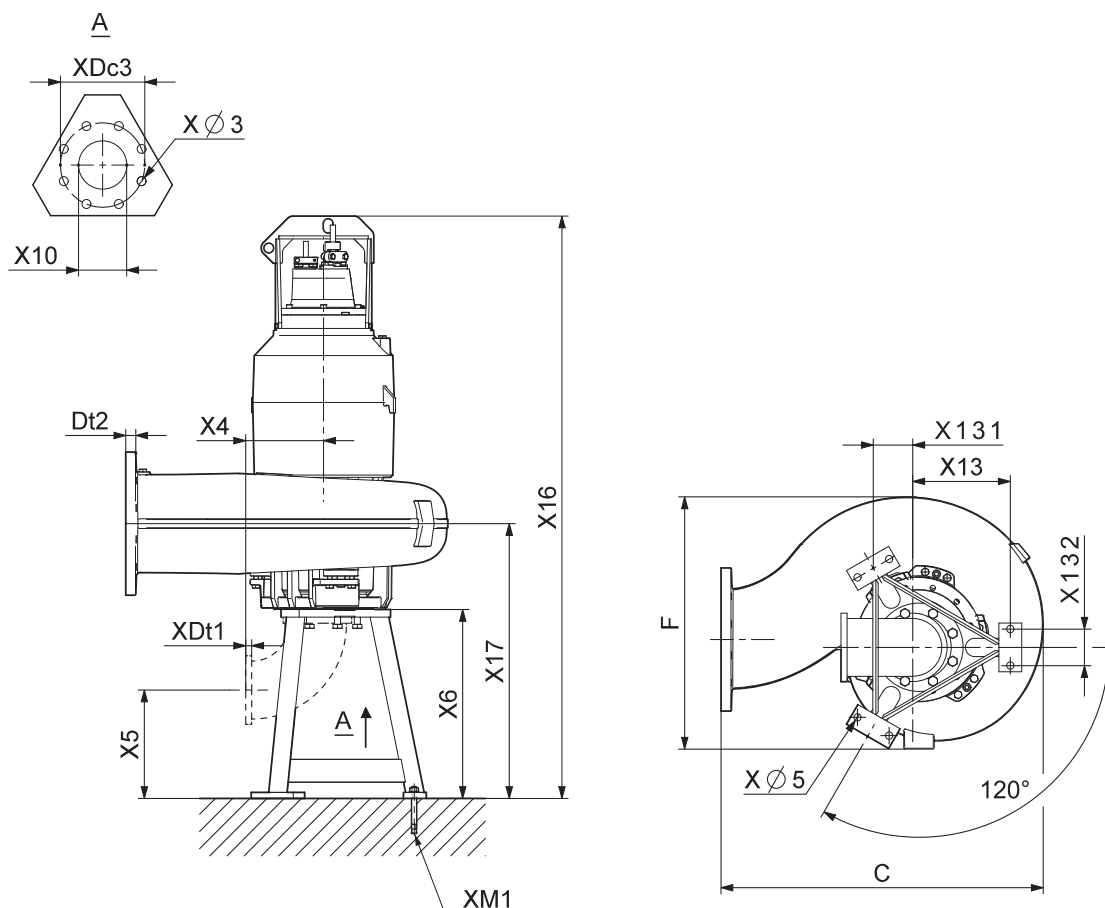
Габаритные размеры, установка на автоматической трубной муфте
